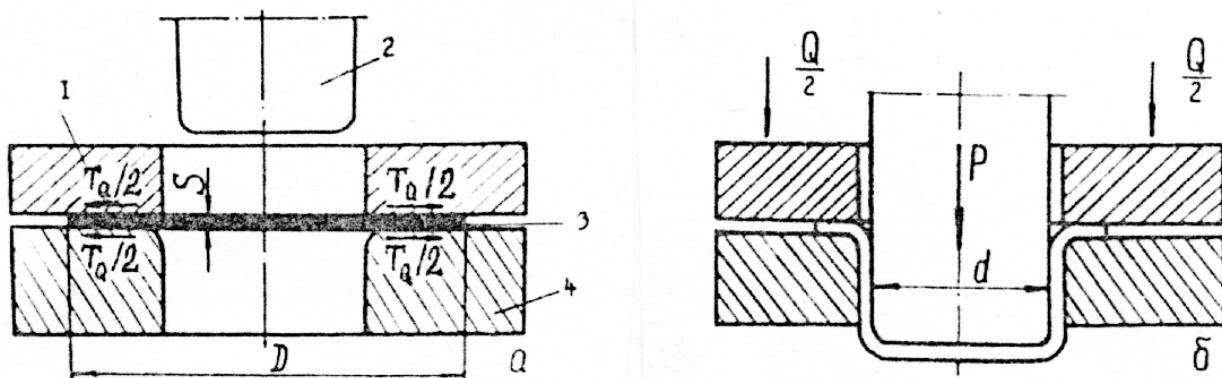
Операції витягання виробу: а - початкова; б - поточна: 1 - притиск; 2 - пуансон для витягання; 3 - заготовка; 4 - матриця
